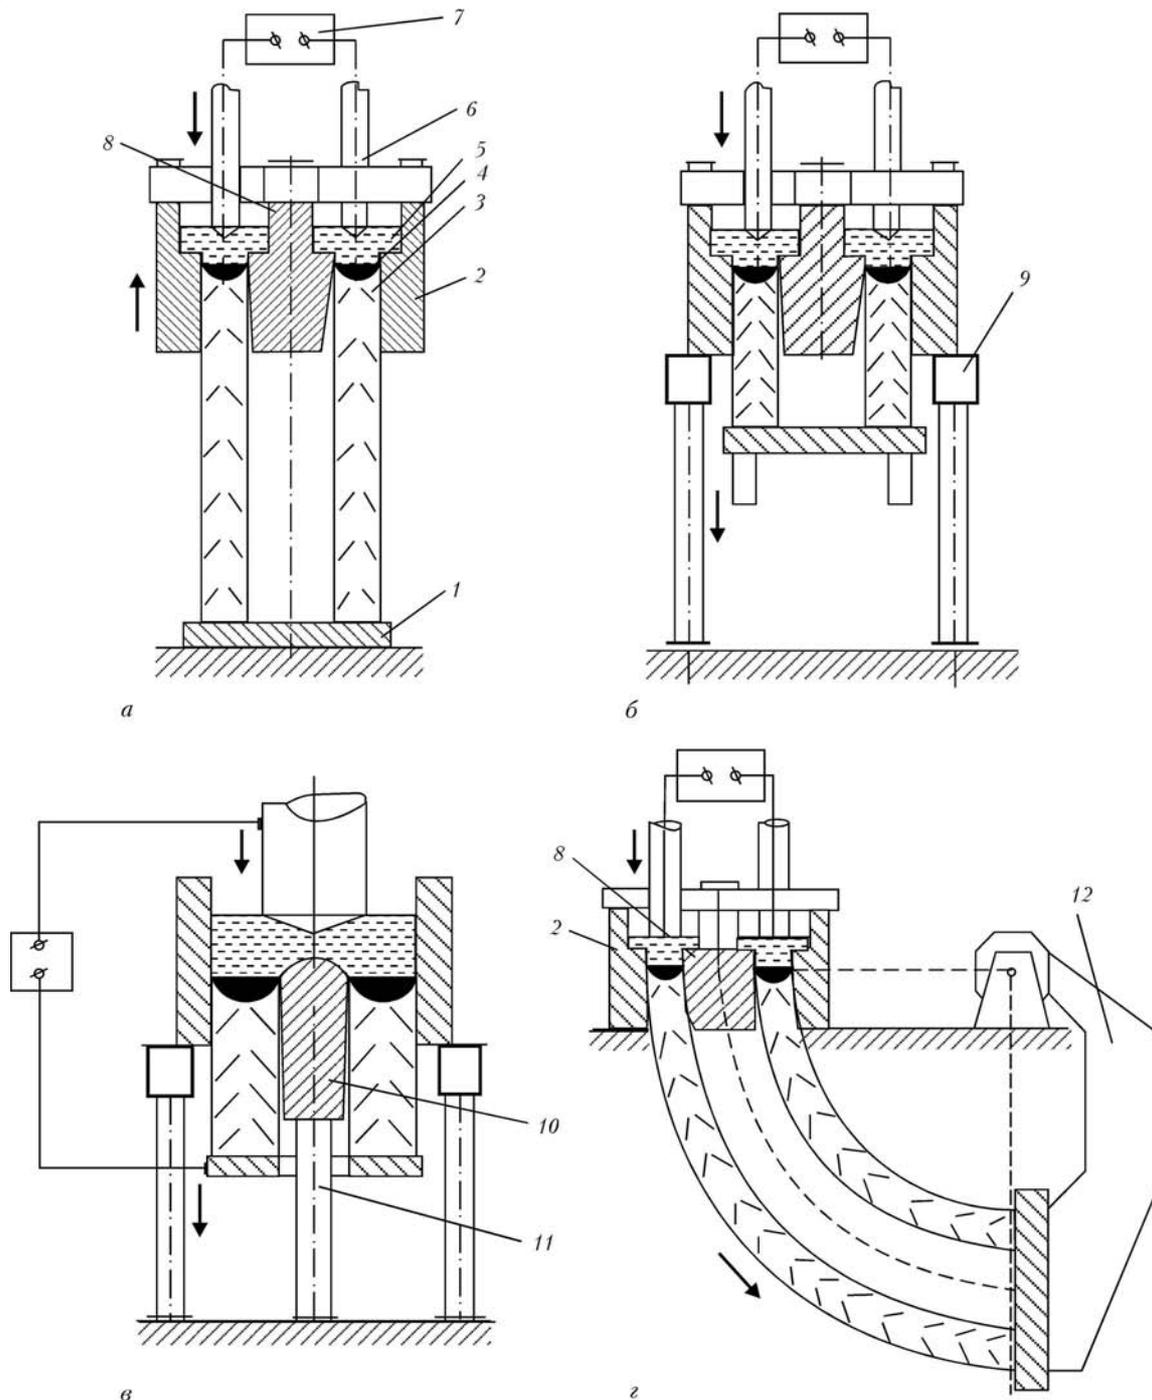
Схемы ЭШЛ с относительным перемещением кристаллизаторов и полых заготовок: *а* — с неподвижной выплавляемой заготовкой и перемещающимся вверх блоком кристаллизаторов; *б* — с неподвижным блоком кристаллизаторов и перемещающейся вниз выплавляемой заготовкой; *в* — с перемещающейся вниз выплавляемой заготовкой и неподвижными отдельными наружным кристаллизатором и дорном (электрошлаковая прошивка); *г* — с неподвижным блоком кристаллизаторов и перемещающейся по дуге окружности выплавляемой заготовкой; 8 — дорн, соединенный в блок с наружным кристаллизатором; 9 — стационарная платформа для кристаллизатора; 10 — дорн для электрошлаковой прошивки; 11 — шток дорна; 12 — механизм вытягивания заготовки по дуге окружности
